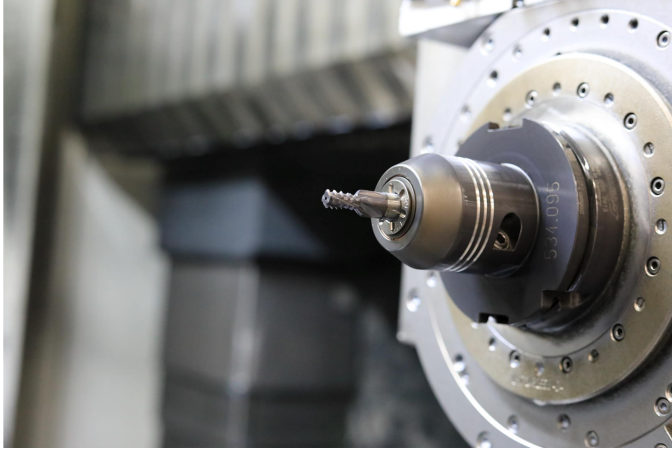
Gewindefräser TC620 Supreme in der Aufspannung
